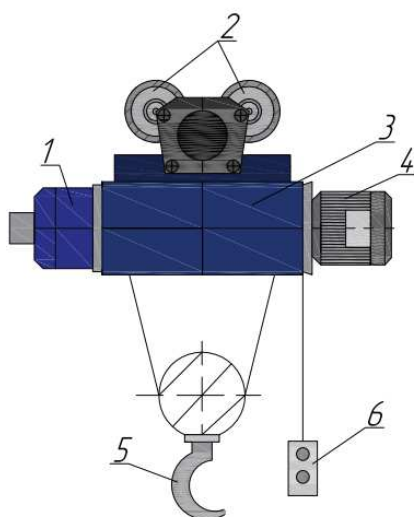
Общий вид электрической тали: 1 –редуктор; 2 – колеса; 3 – барабан; 4 – электродвигатель; 5 – крюк; 6 – кнопочный пост управления
